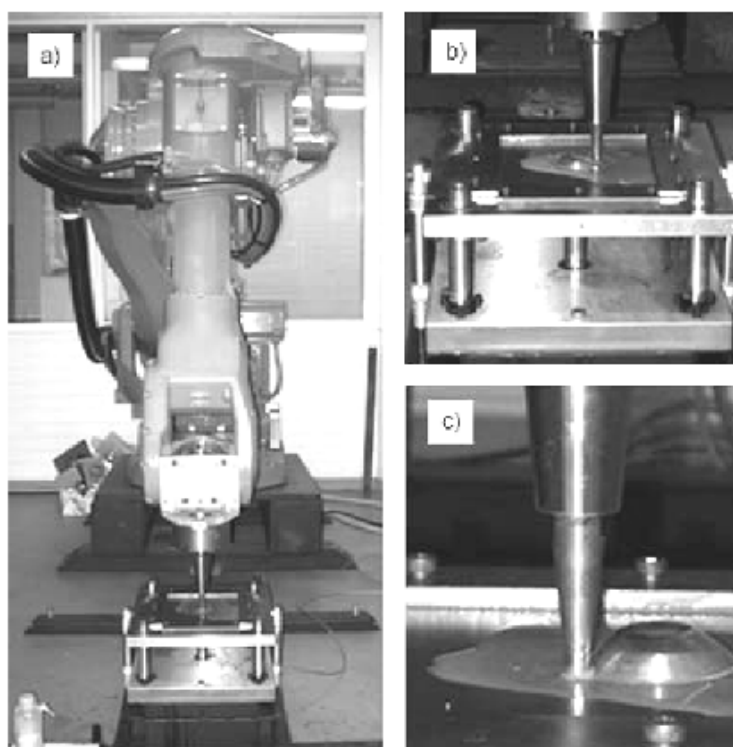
Setup* teste para Estampagem Incremental com um robô industrial: a - célula do robô; b - mesa de estampagem; c - ferramenta de estampagem (Lamminen, 2005).
